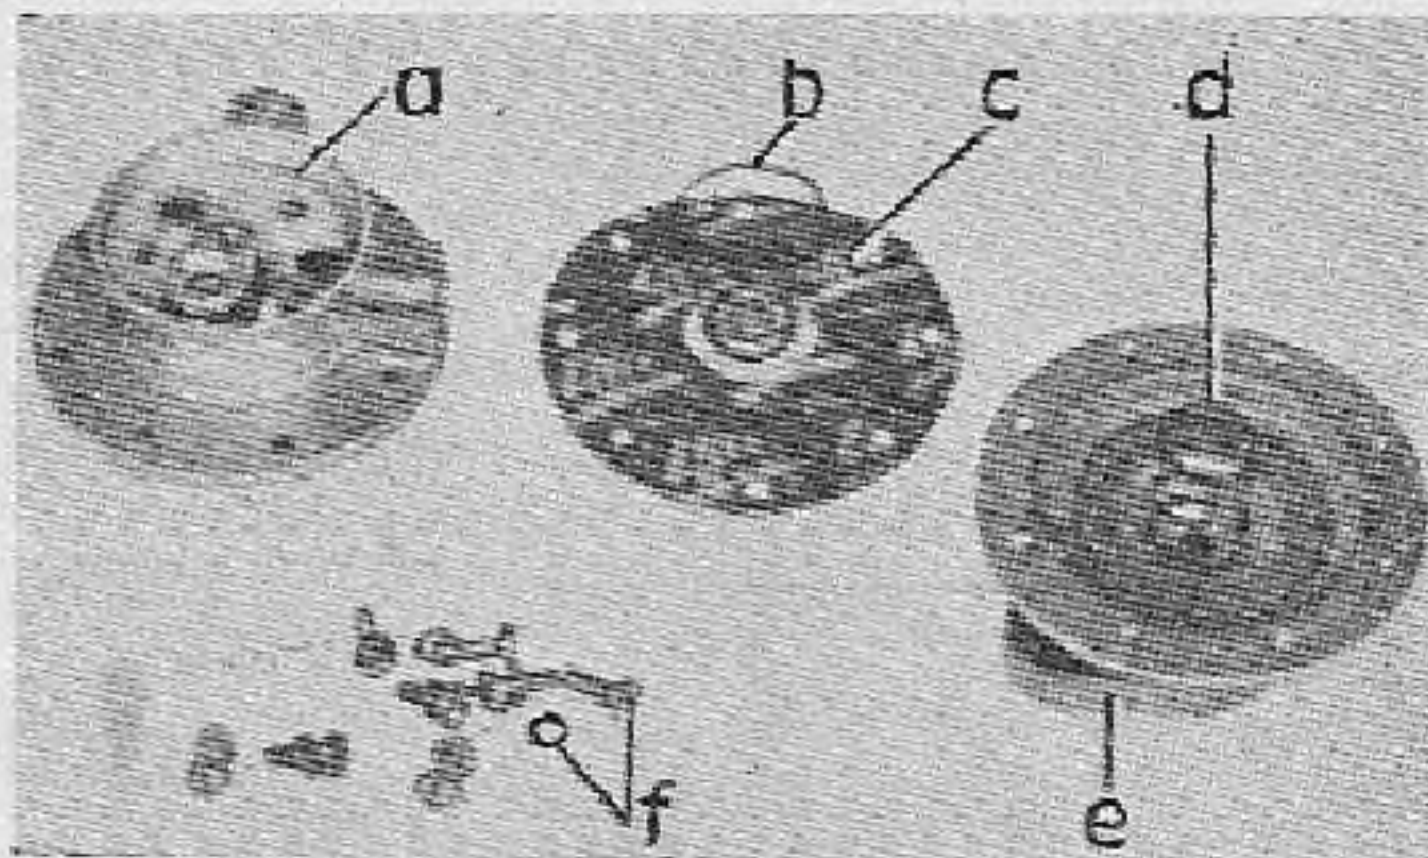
Diafragma (membrana) de la bomba de combustible.
